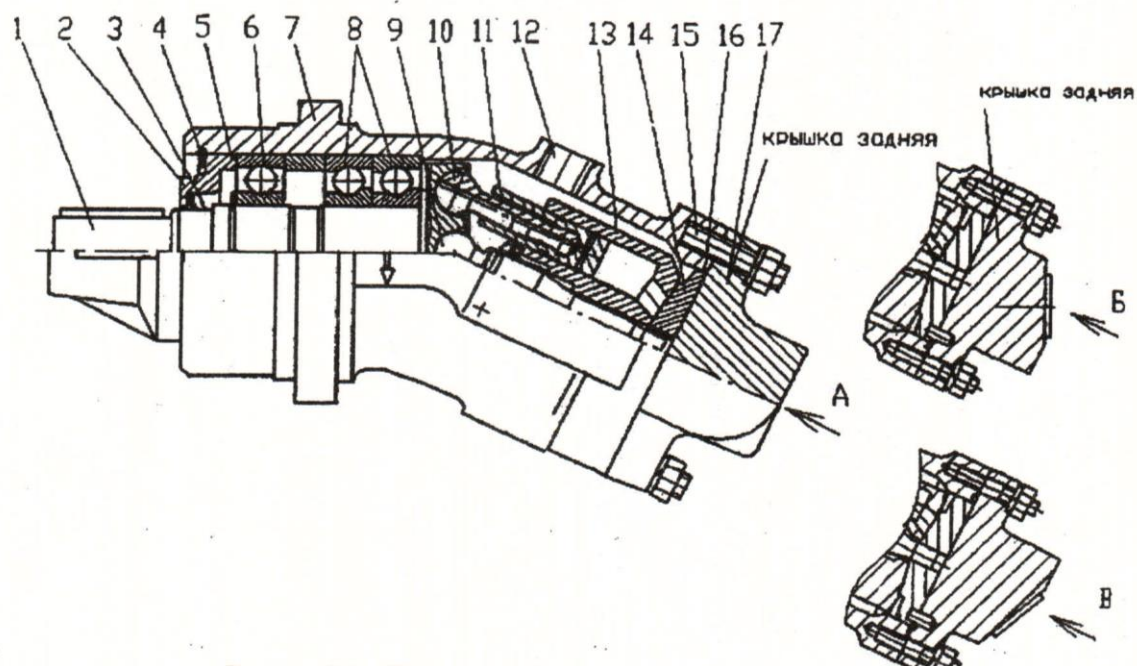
Насос (мотор) с шариковыми радиально-упорными подшипниками
